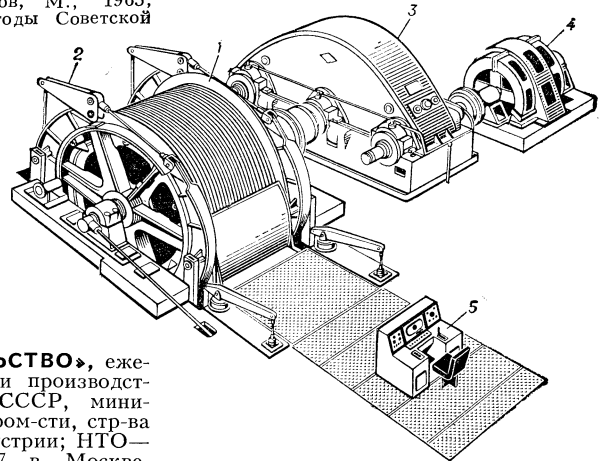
Подъёмная машина с цилиндрическим барабаном: 1 — аппарат наливки; 2 — тормозное устройство; 3 — редуктор; 4 — электродвигатель; 5 — пульт управления.
